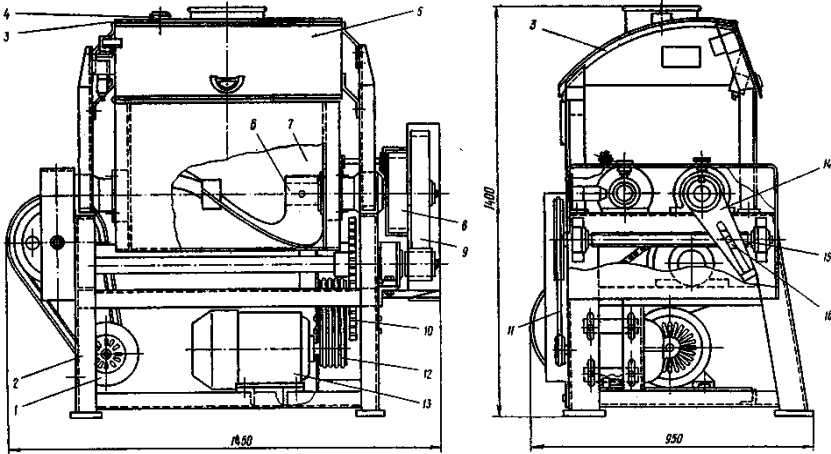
Тістомісильна машина ТМ-63Г: 1 - електродвигун; 2 - станина; 3 - кришка; 4 - патрубок для подачі рідин; 5 - дверцята; 6 - місильна лопата; 7 - робоча камера; 8, 9 - шестерні; 10, 11 - ланцюгові передачі; 12 - клиноремінна передача; 13 - електродвигун; 14 - повідок; 15 - ходовий гвинт; 16 - повідкова гайка
